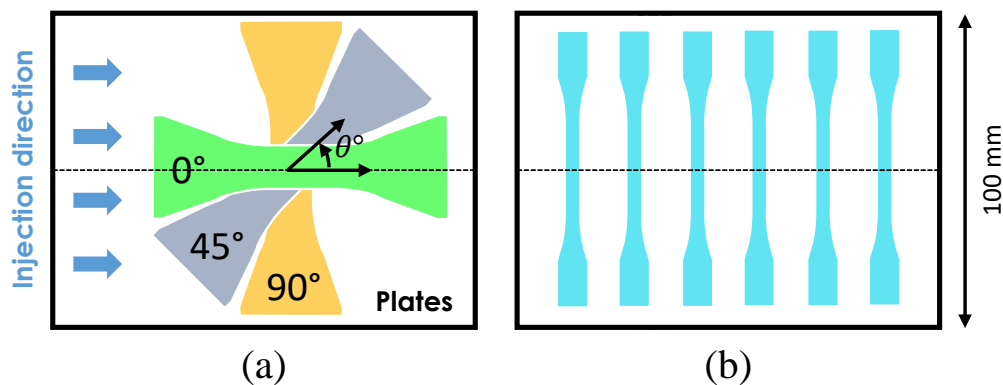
Angles d'extraction des éprouvettes de composite et de matrice pure par rapport à la direction d'injection et à la largeur des plaques. Éprouvettes issues de plaques (a) avec et (b) sans fibres.
